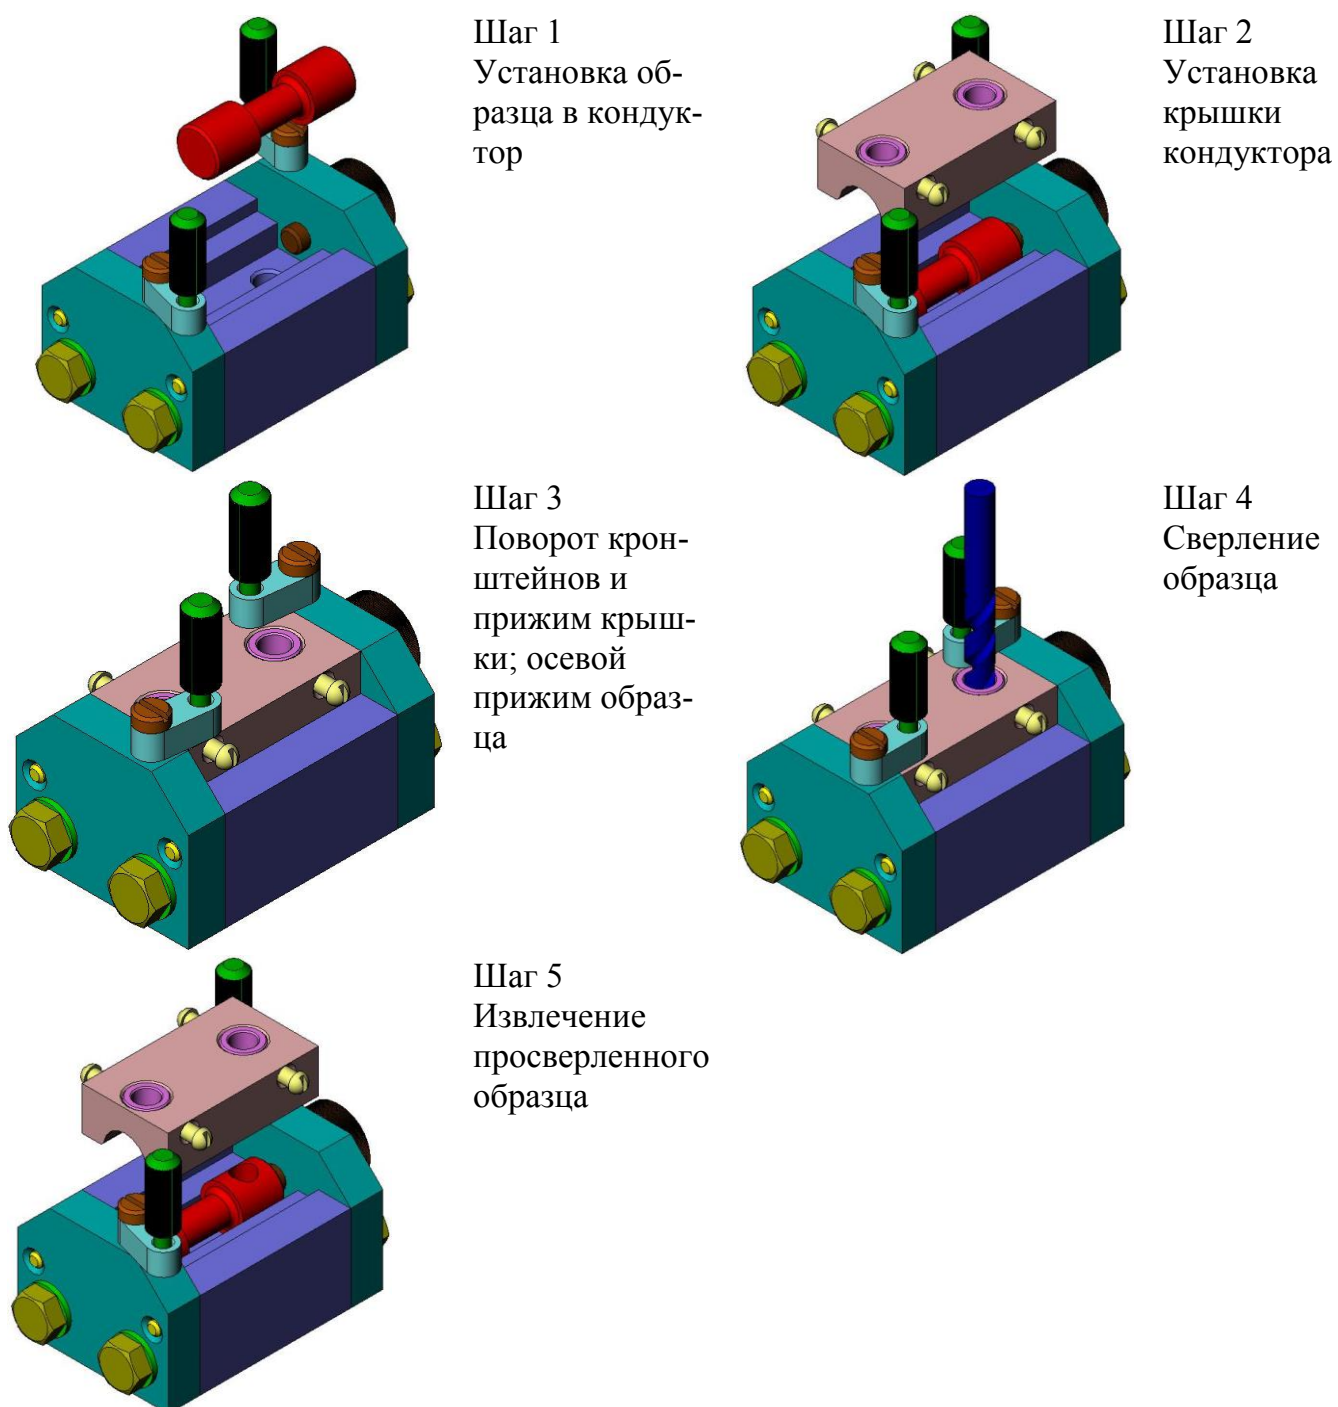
Порядок работы с кондуктором при изготовлении образцов
